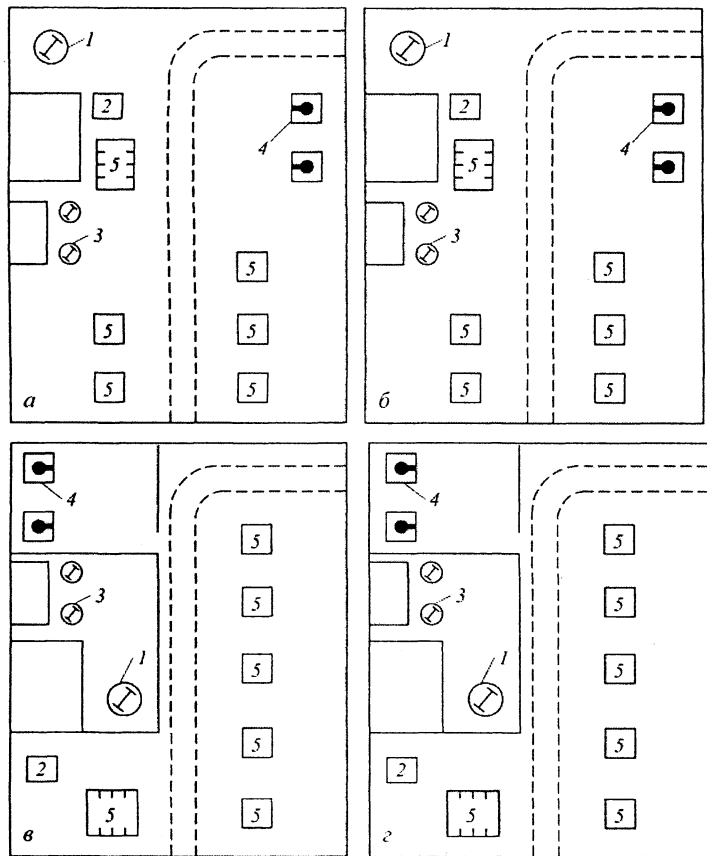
План участка литейного цеха: а – существенный вариант; б – с заменой оборудования без перепланировки; в – с перепланировкой; г – с изменением оборудования и перепланировкой; 1, 3 – бегуны; 2 – машина формовочная; 4 – печь плавильная; 5 – формовка, сборка и заливка форм
